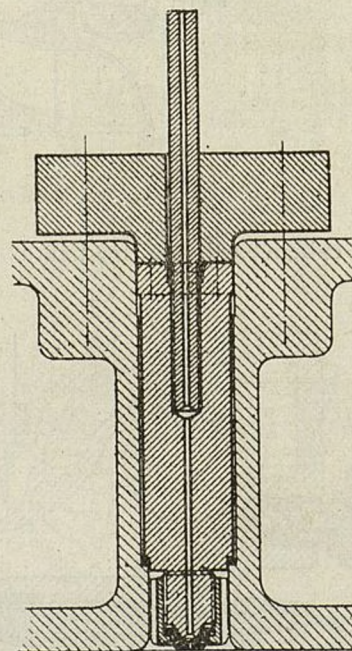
Tobera abierta del motor Diesel M. A. N. sin compresor (taller de Augsburg)
